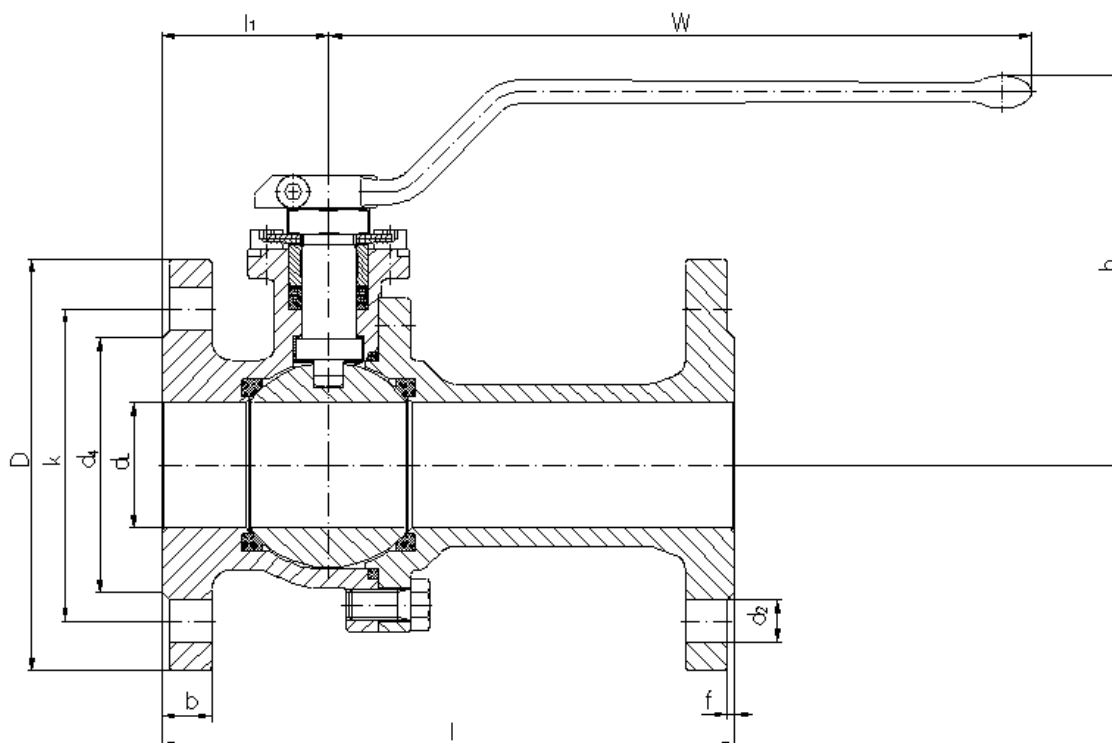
Kugelhahn mit Flanschschluß nach DIN EN 1092-1 Form B1; Baulänge Grundreihe 28 (lang) nach EN 558-1 (F17 nach DIN 3202 Teil 1)
